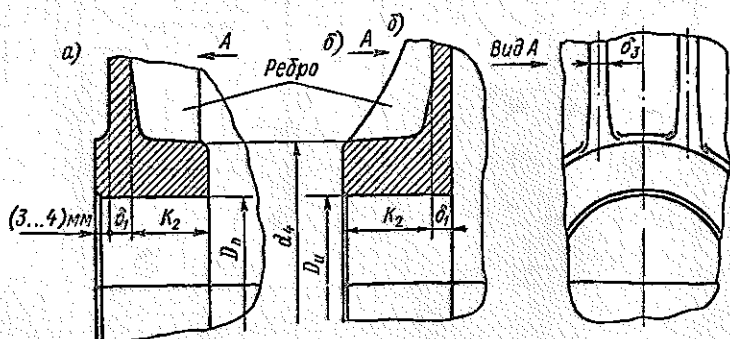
Приливы с ребрами жесткости для подшипниковых гнезд: а — прилив внутри корпуса и крышки редуктора; б — прилив снаружи корпуса и крышки редуктора с ребрами жесткости
